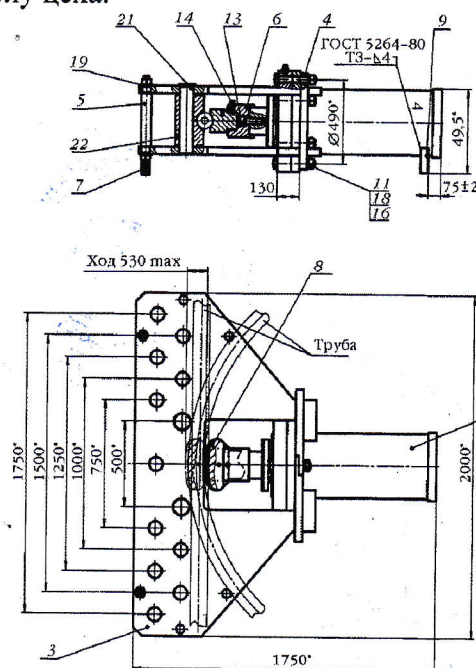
Трубогиб: 1 – гидроцилиндр; 2 – центральный силовой сегмент; 3 – верхняя плита; 4 – упор; 5 – боковой поворотный силовой сегмент; 6 – стяжная шпилька; 7 – гайка; 8 – шпандырь; 9 – стопор; 10 – проточка; 11 – втулка; 12 – стяжное кольцо; 13 – подставка; 14 – стяжные болты
